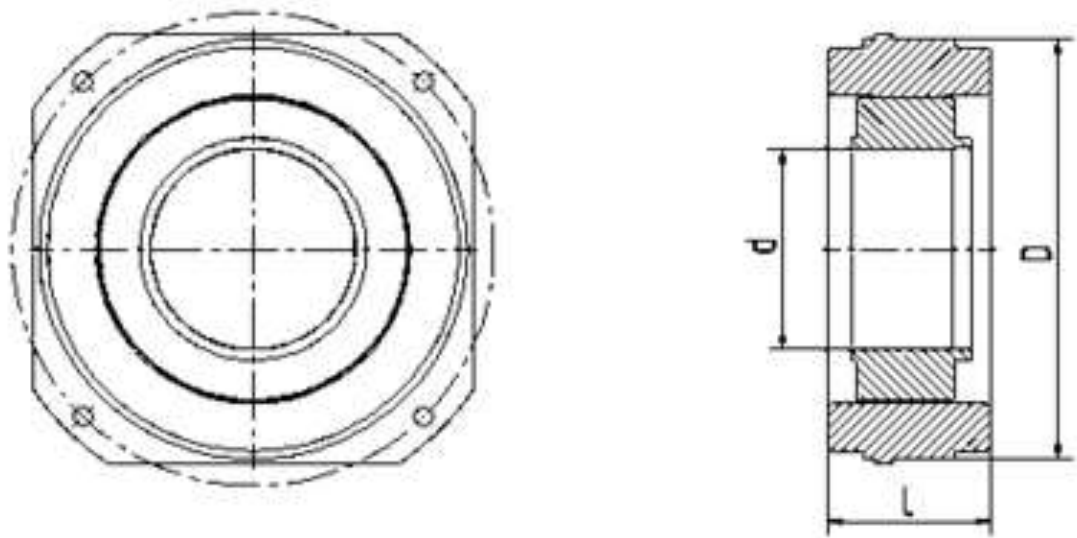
Двигатель ДБМ с пазовым статором
